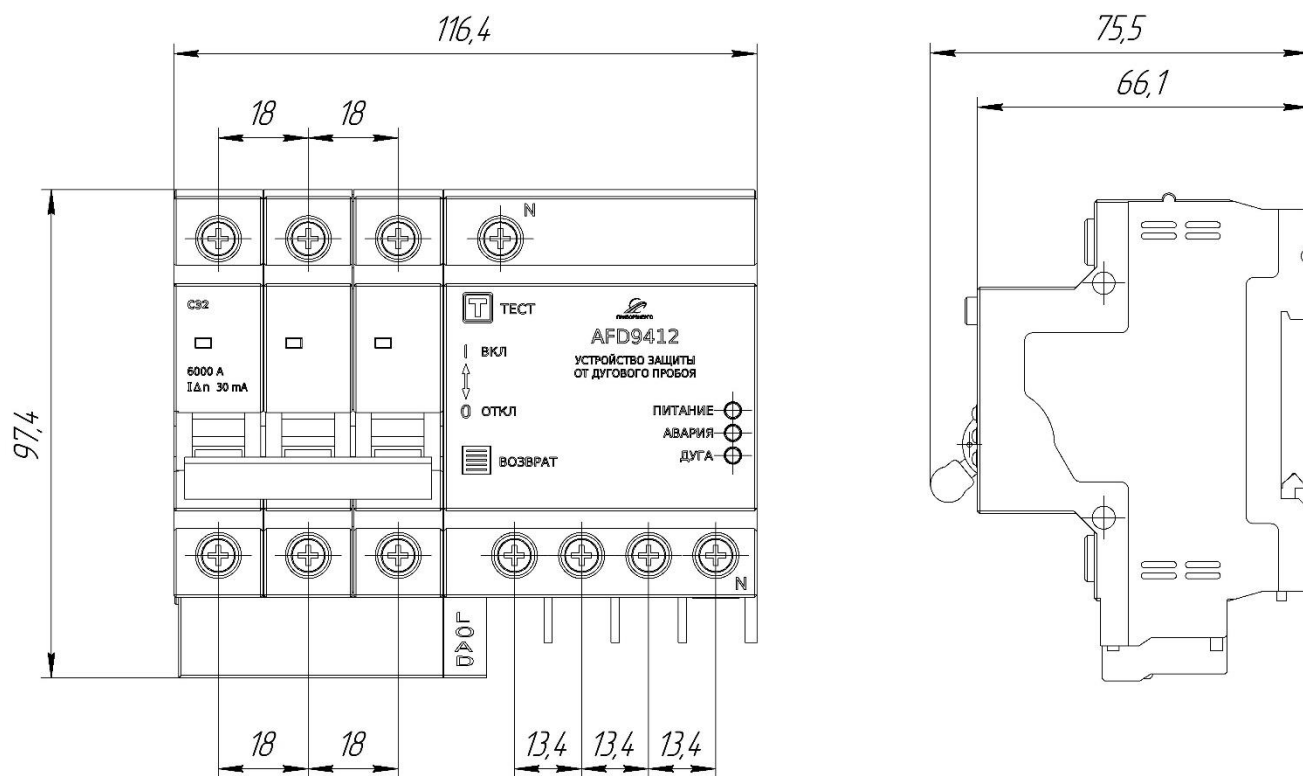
Габаритные размеры устройства защиты от дугового пробоя AFD9412
